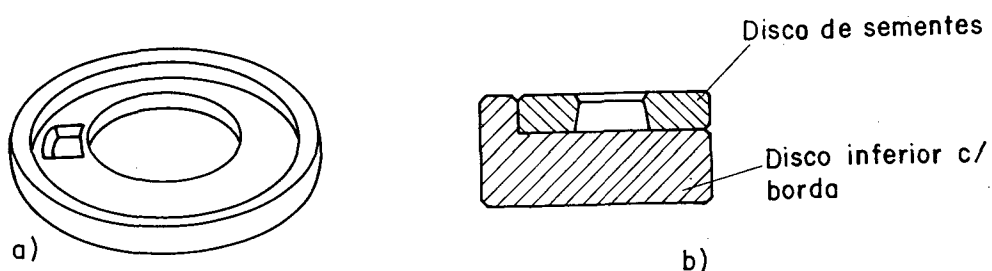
a) Disco inferior com borda; b) Detalhe de montagem [25].
